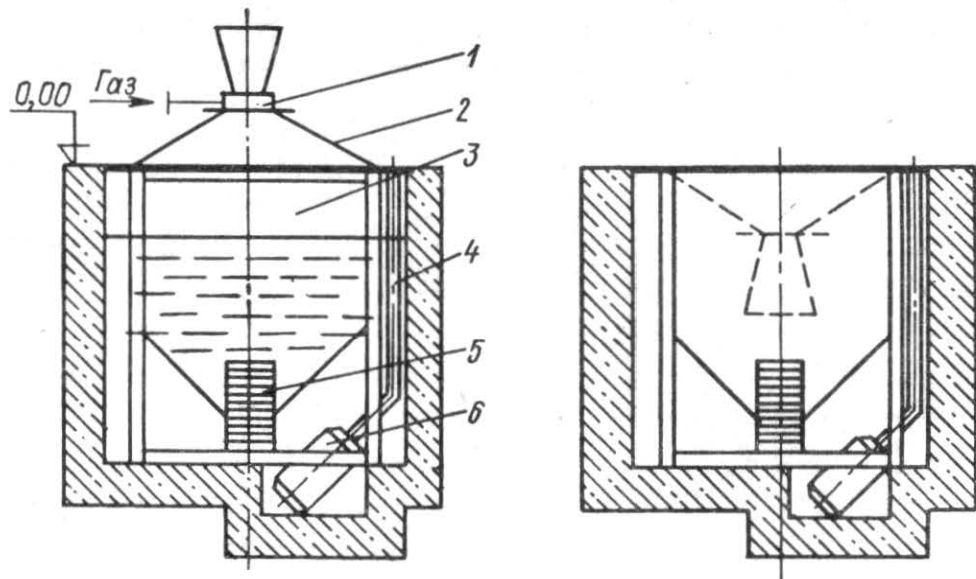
Схема малогабаритної установки для отримання металевого литого дробу
